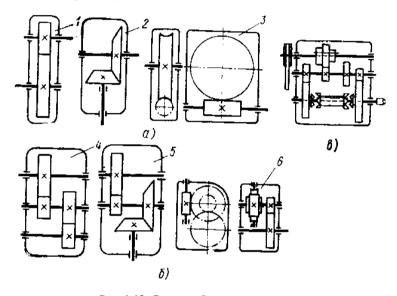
Схемы зубчатых редукторов: а – одноступенчатые; б – двухступенчатые; в – коробка передач;
